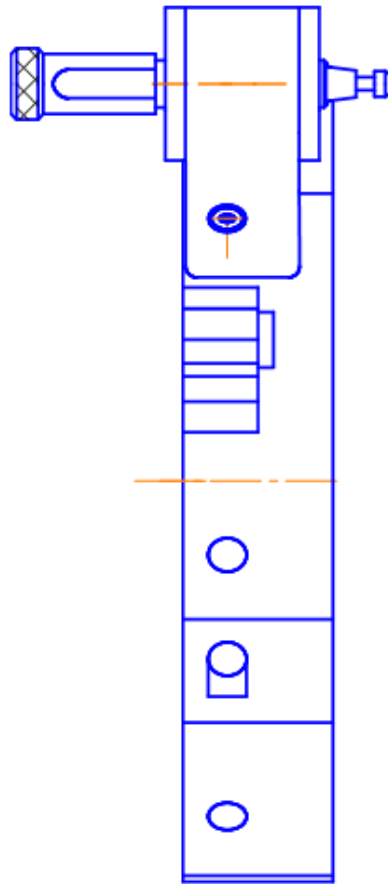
Схема крепления инструментального блока на револьверной головке, вид с торца
